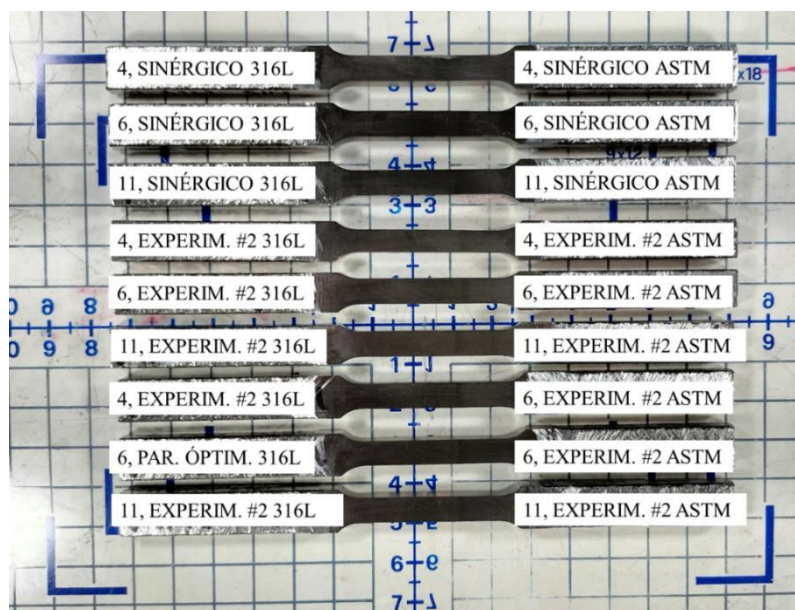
Probetas para ensayos de tensión uniaxial de la unión disímil ASTM A516 Gr. 70 / AISI 316L.
